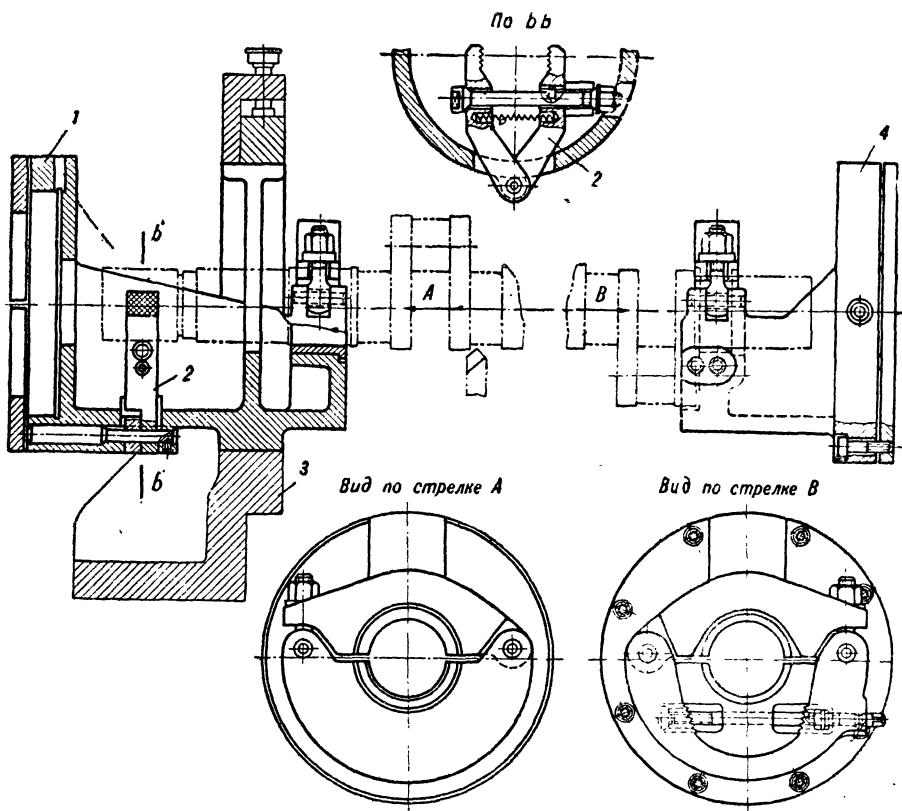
Приспособление для обработки коренных шеек коленчатого вала,
